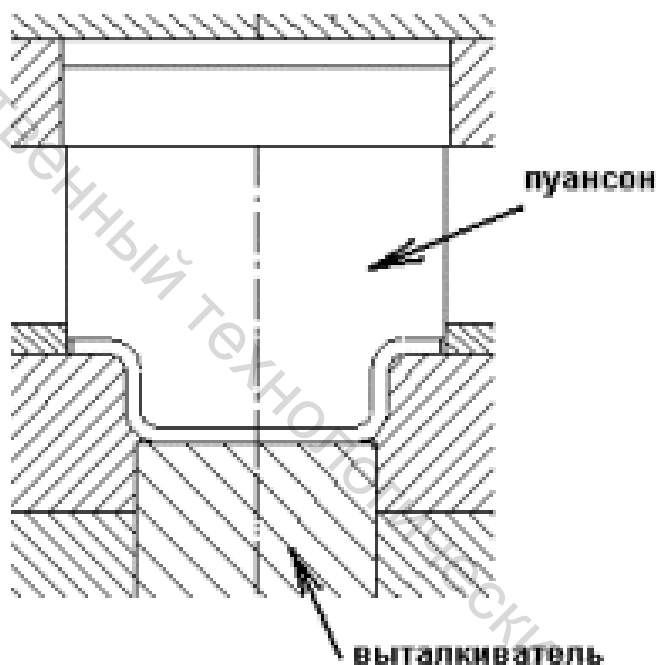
Разрез рабочей зоны гибочного штампа
